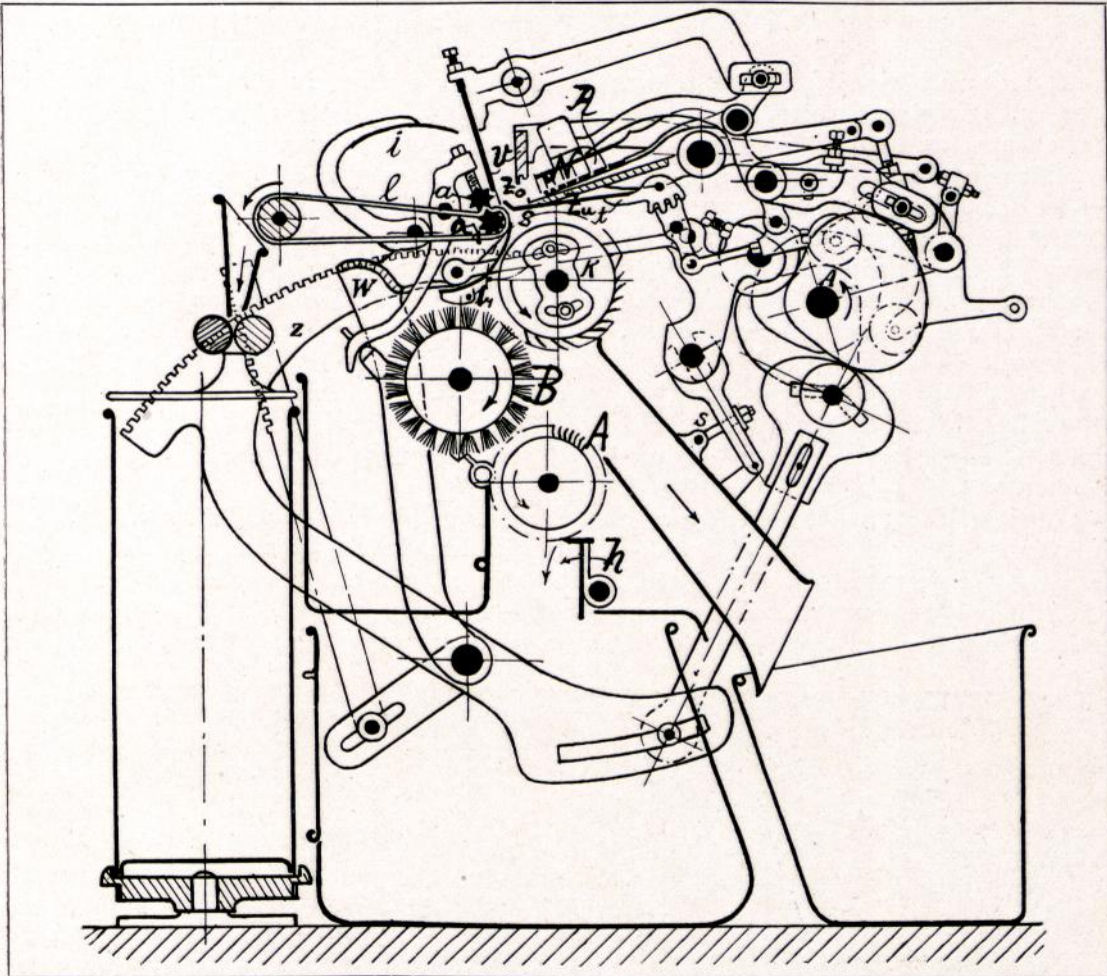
Wollkämmaschine der Elsäss. Maschinenbaugesellschaft in Mülhausen.
